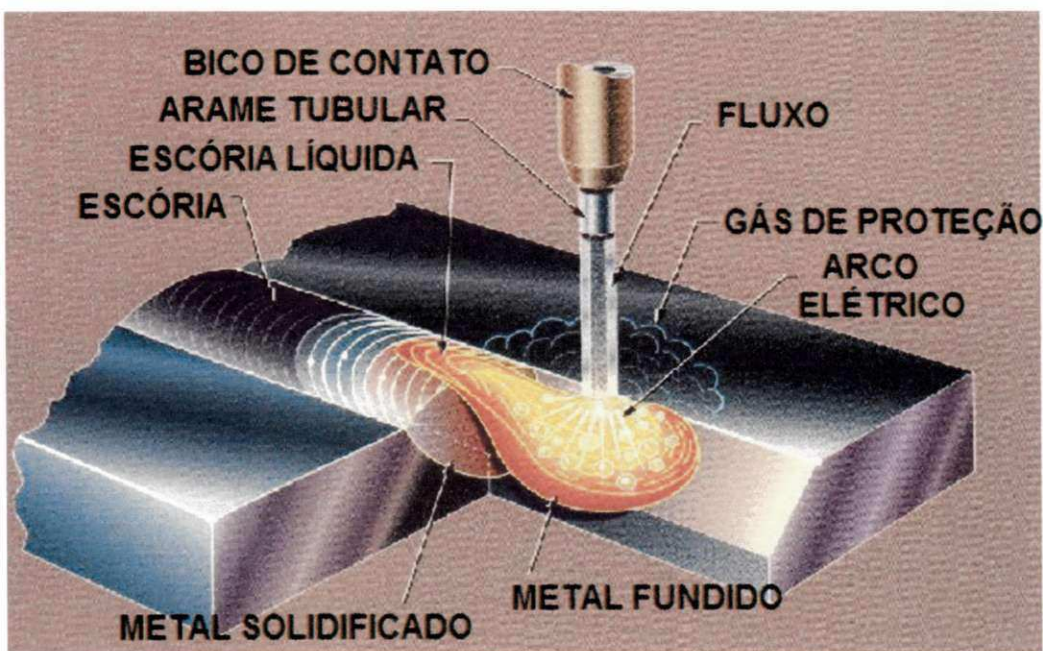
Esquema de soldagem com arame tubular pelo processo FCAW-S adaptado de Welding Handbook (1991).
